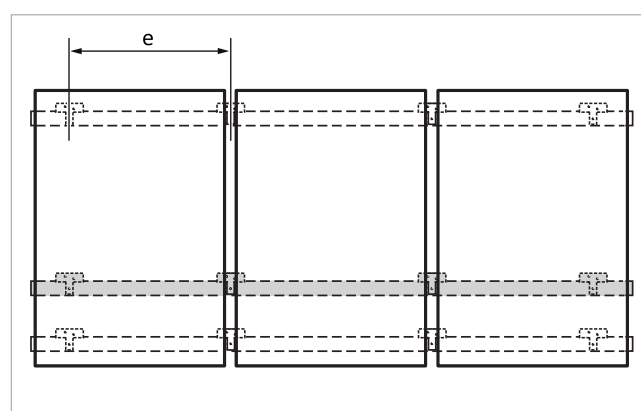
Traversa supplementare di bloccaggio (montaggio affiancato)
